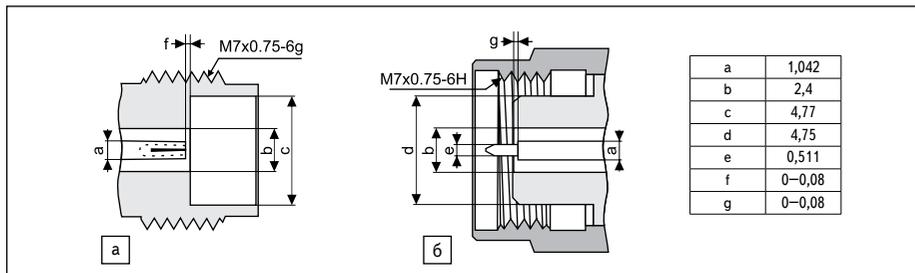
Интерфейс 2,4-мм соединителя: а) розетка; б) вилка
